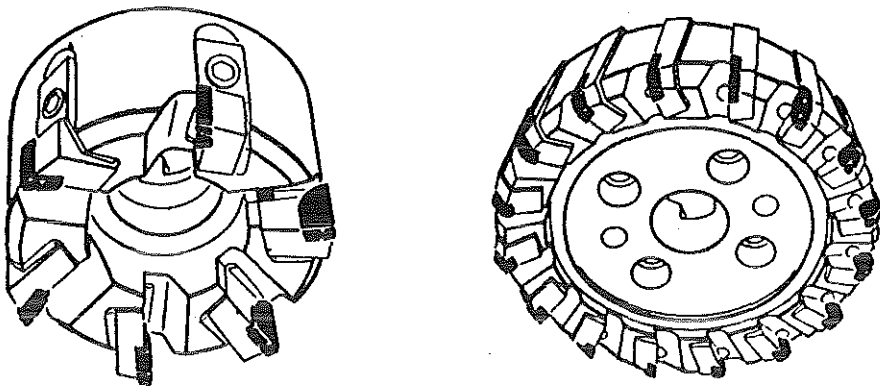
Fresas com pastilhas de metal soldada em uma face.
